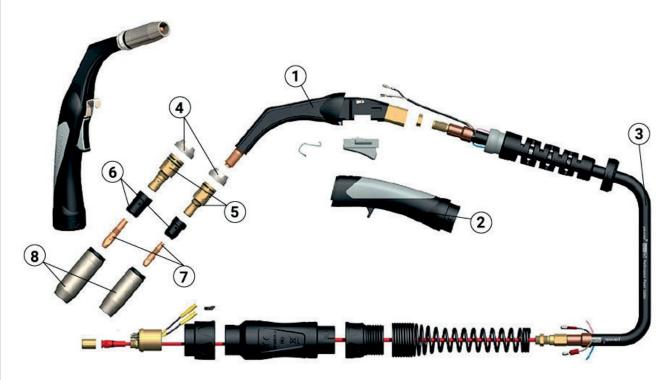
Принципова схема пальника XP8G2 350A Parweld: 1 – гусак, 2 – руків'я, 3 – шланг-пакет, 4 – кільце-ізолятор, 5 – вставка, 6 – газорозподілювач, 7 – накінечник, 8 – сопло
